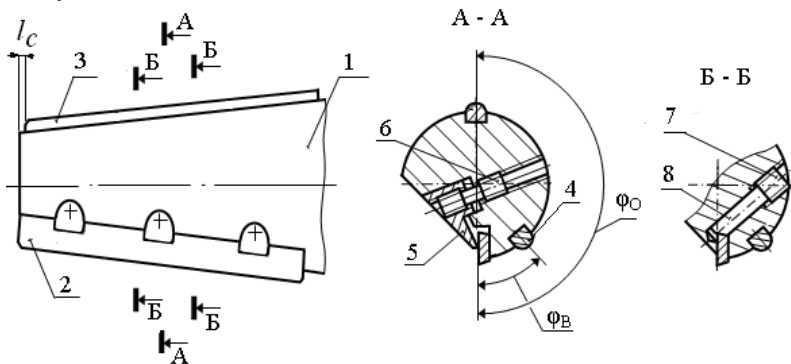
Конструкция однолезвийной развертки со сменной твердосплавной пластиной фирмы Maral
